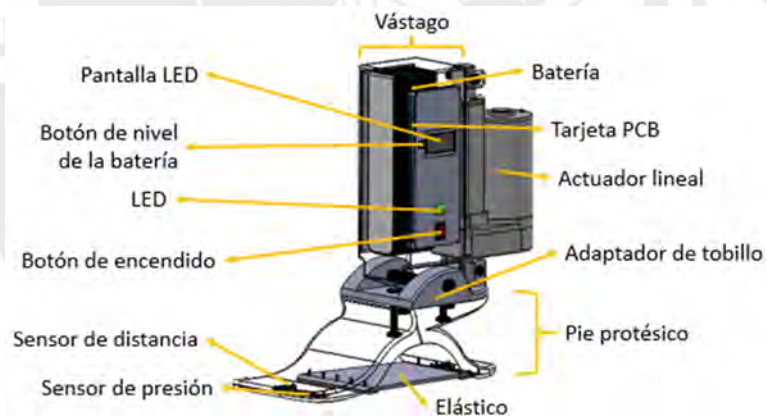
Partes del diseño final de la prótesis – vista isométrica.
